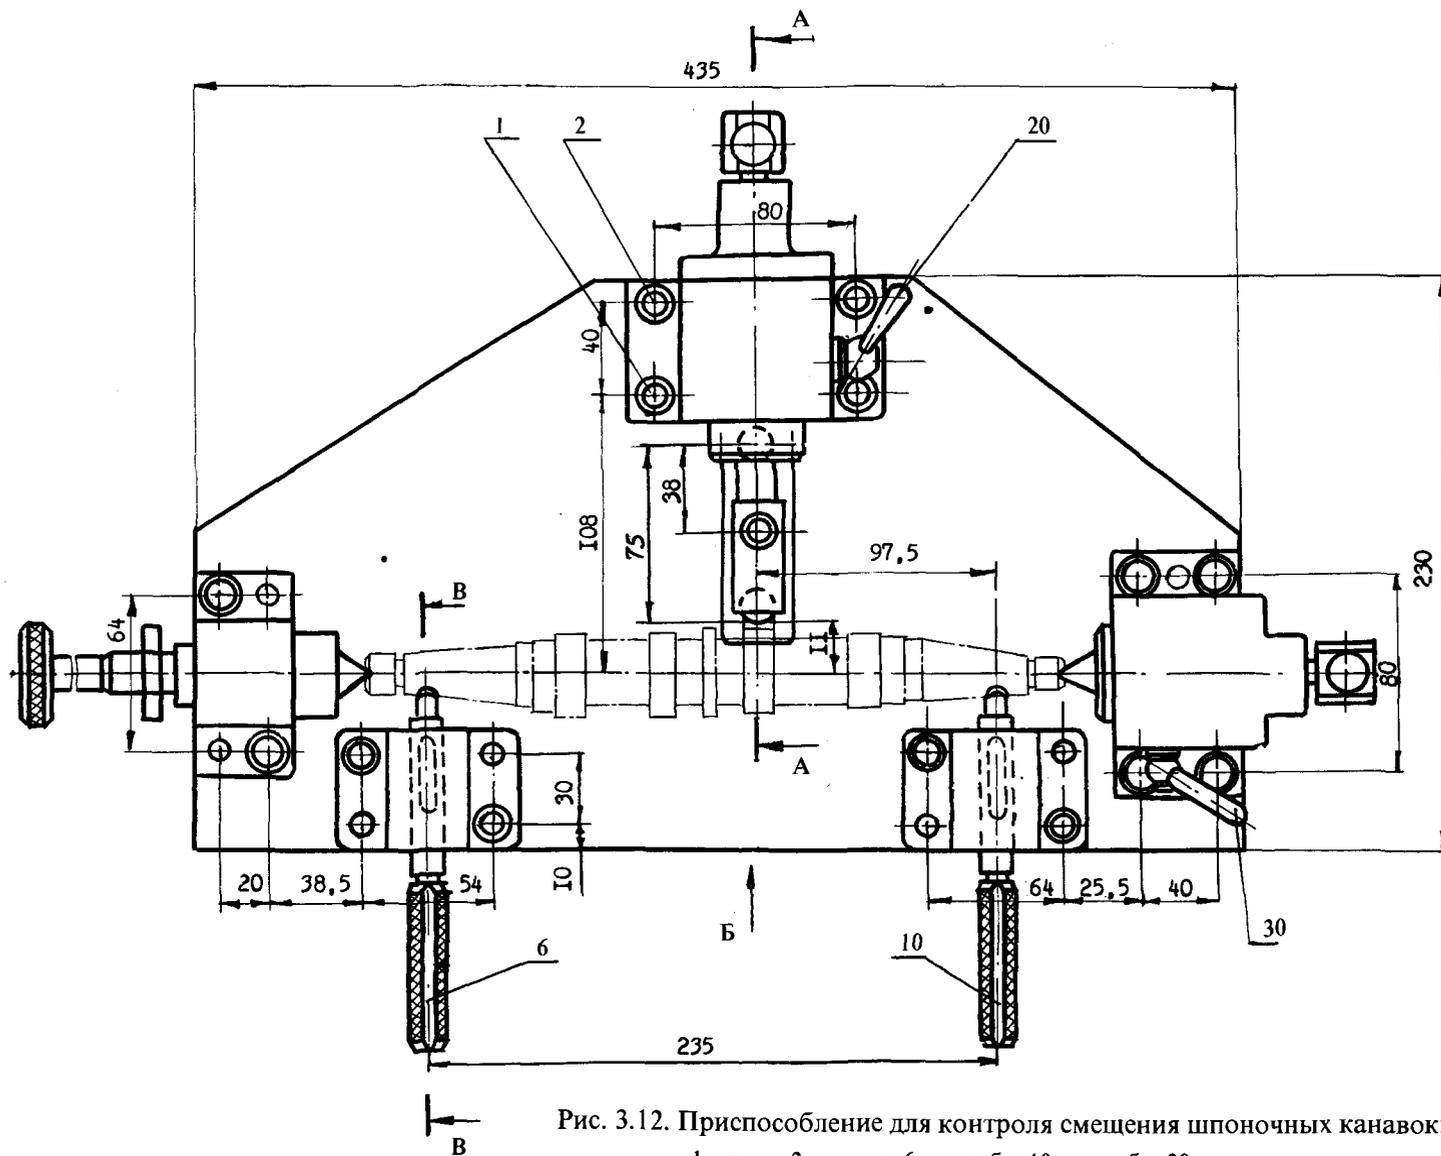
Приспособление для контроля смещения шпоночных канавок:
